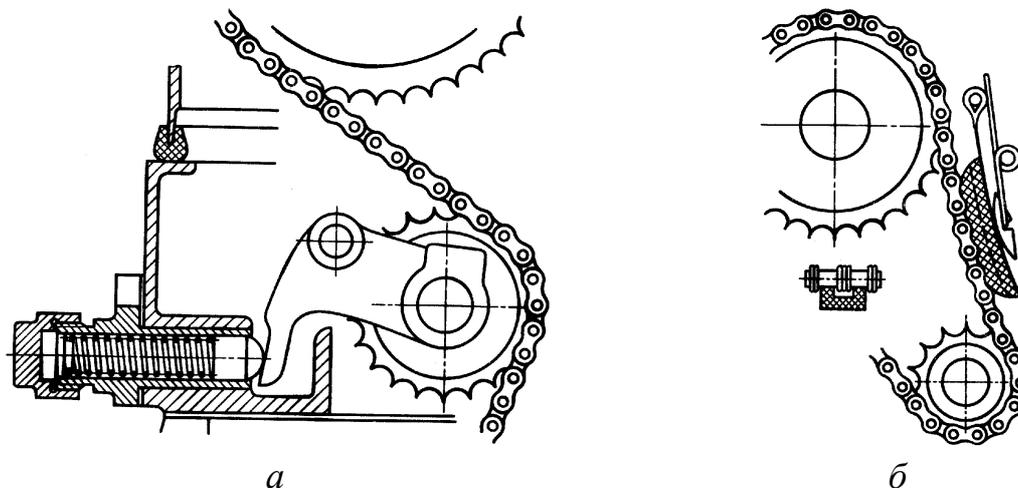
Натяжное устройство и гаситель вибрации цепной передачи
